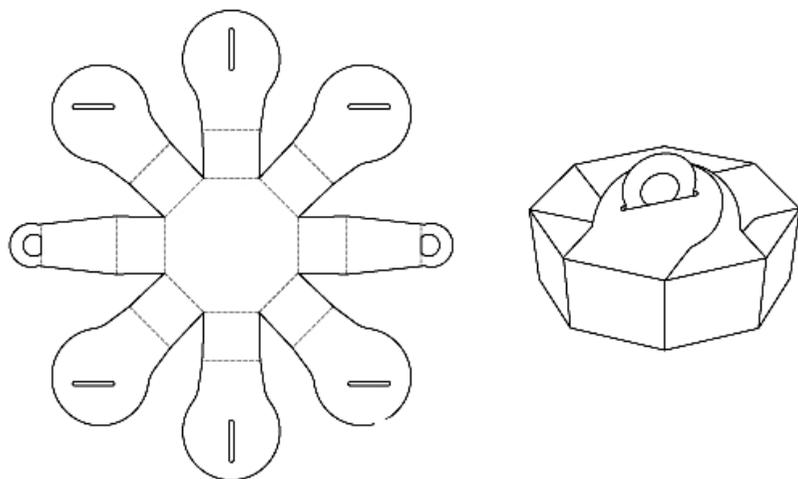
Упаковка «Восьмиугольная коробка с ручкой».
